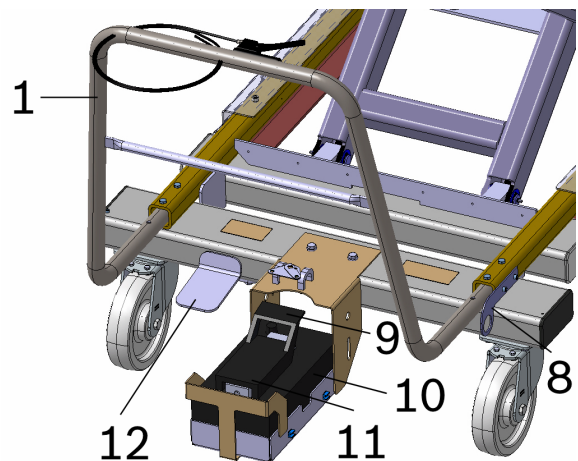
Collegamento del tubo flessibile dell'aria compressa al piano elevatore a pantografo
